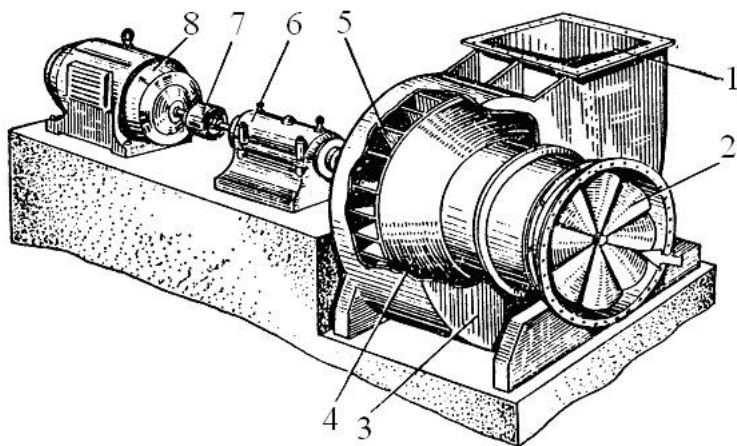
Дымосос (дутьевой вентилятор) одностороннего всасывания: 1 – выходной патрубок; 2 – поворотные лопатки направляющего аппарата; 3 – улиткообразный кожух; 4 – ротор; 5 – рабочее колесо; 6 – корпус подшипников; 7 – соединительная муфта; 8 – электродвигатель
